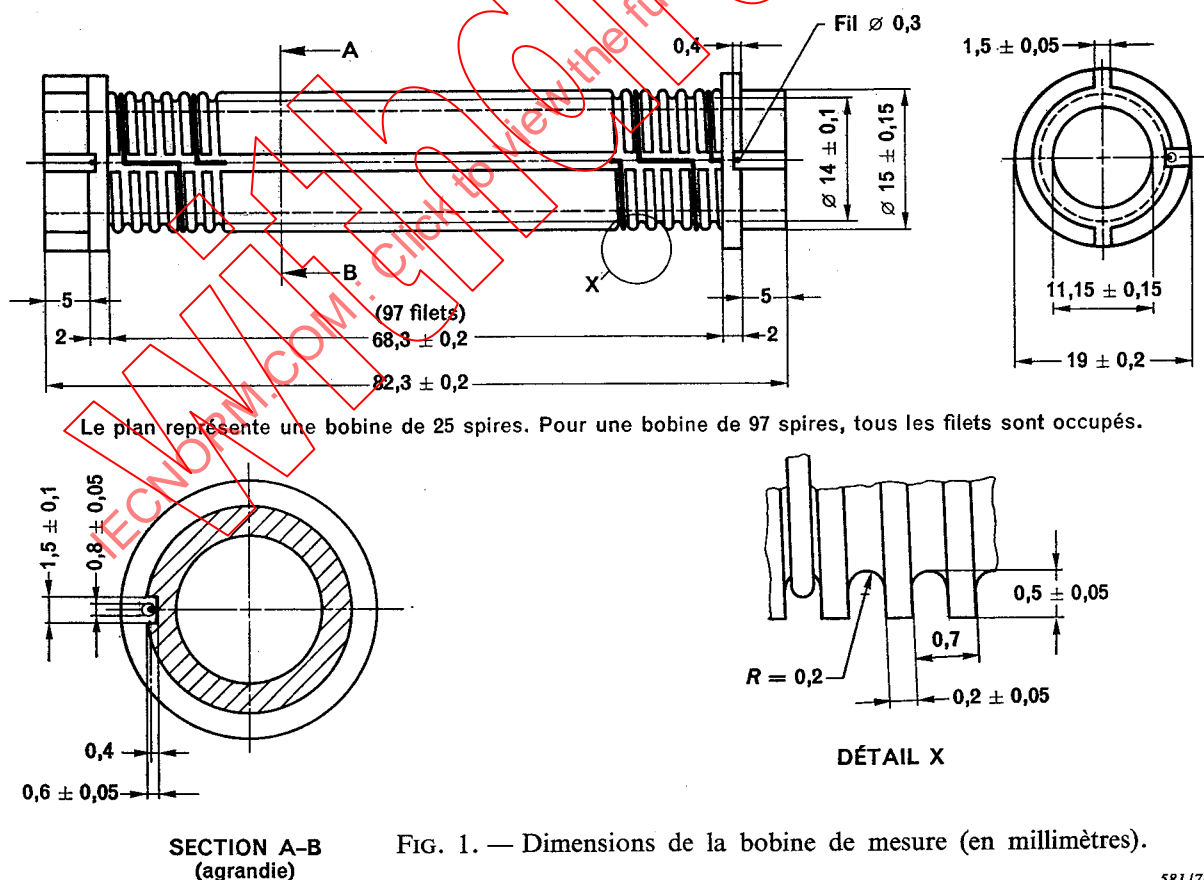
Dimensions de la bobine de mesure (en millimètres).
